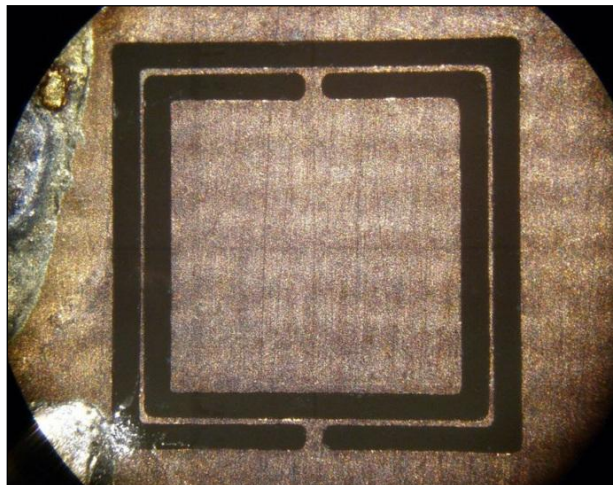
Detalle de un CSSR y una soldadura del circuito 6.
